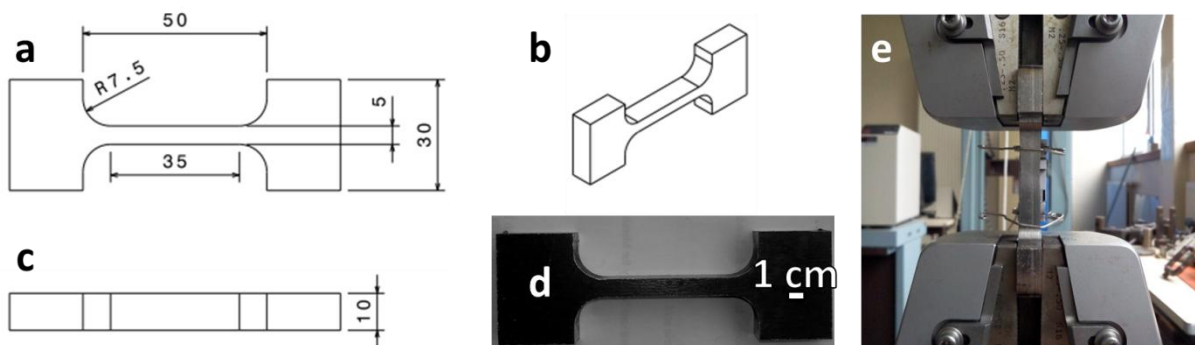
Vue de face (a), vue isométrique (b), vue de dessus (c) du plan d'usinage des éprouvettes de traction ainsi qu'une vue de face d'une éprouvette de traction de métal de base après usinage (d) et éprouvette de traction placée dans les mors équipé d'un extensomètre (e)
